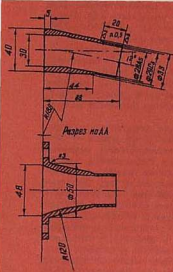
Размеры и конструкция всасывающей патрубкой ИЖ-57.
